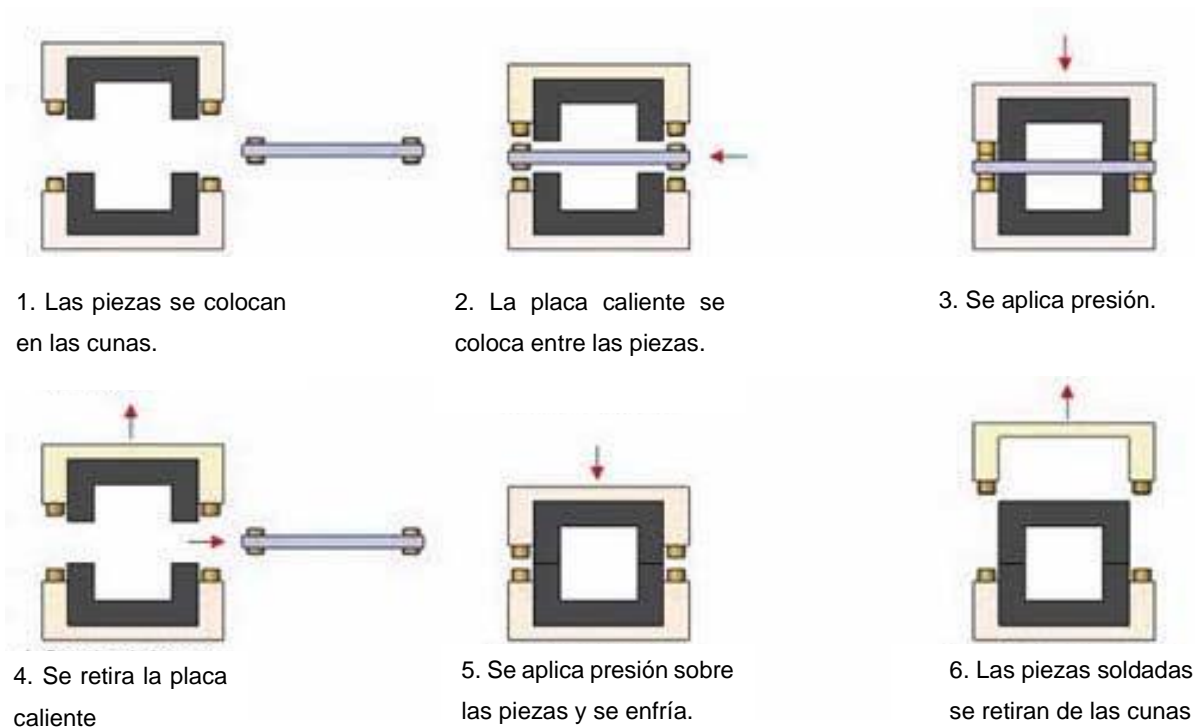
Proceso de soldadura por placa caliente
